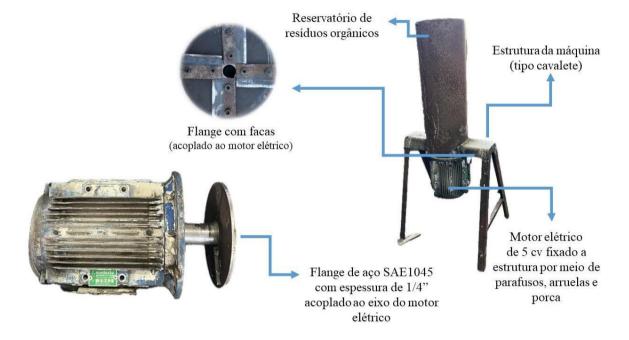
Motor elétrico (usado) de potência 5 cv (4 Kw), tensão 380V, trifásico de alta rotação com flange acoplado ao eixo de saída do motor, fixado a estrutura da máquina. Fonte autoria própria.
